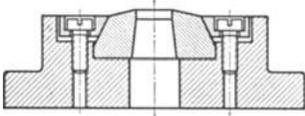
Befestigung der Schnittplatte durch Schräge und Druckstück.
